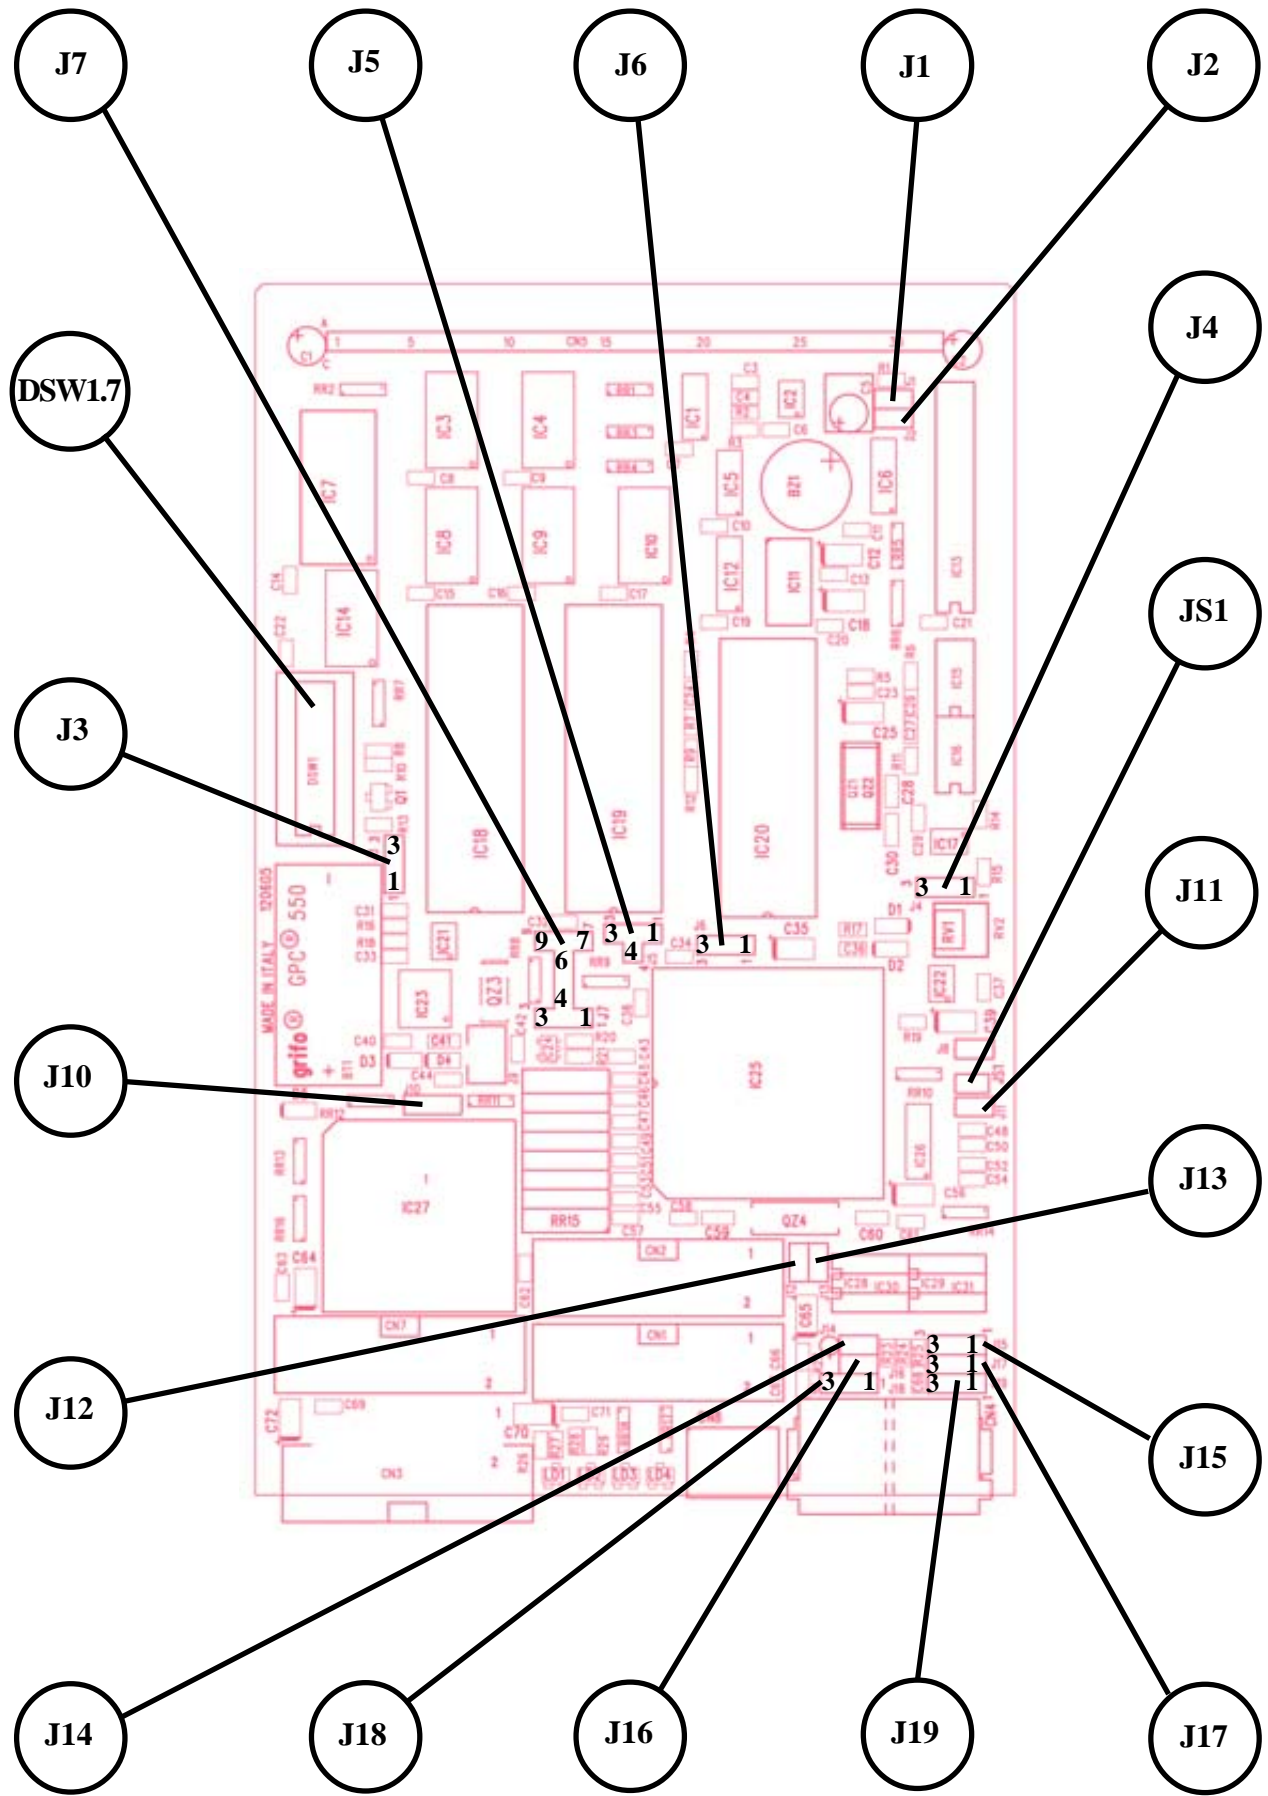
DISPOSIZIONE E NUMERAZIONE JUMPERS
